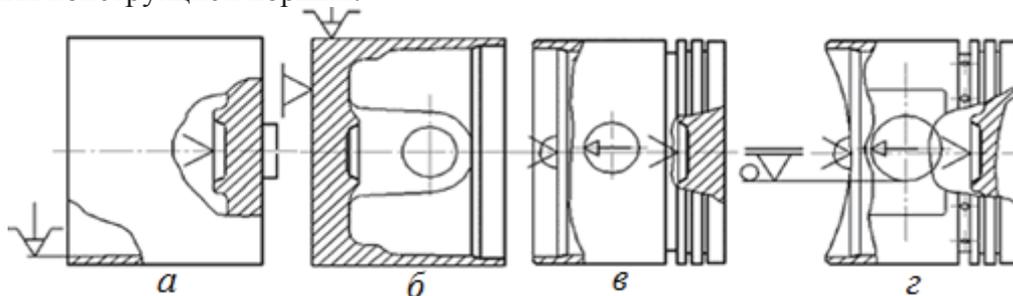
Схемы установки поршня на некоторых операциях механической обработки: а – предварительная токарная обработка заготовки; б – расточка установочных конических поверхностей; в – получистовая обточка головки и юбки, прорезка канавок; з – формирование овально-бочкообразного профиля поршня (утолщенной линией выделены обрабатываемые поверхности)
